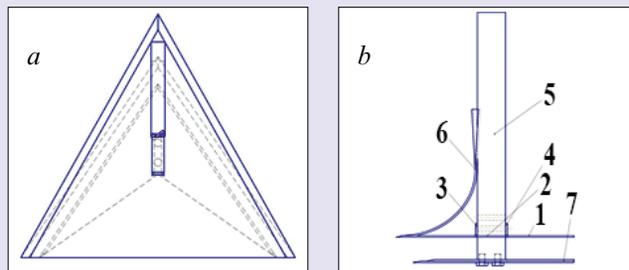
Схема двухъярусной стрелчатой почвообрабатывающей лапы:
